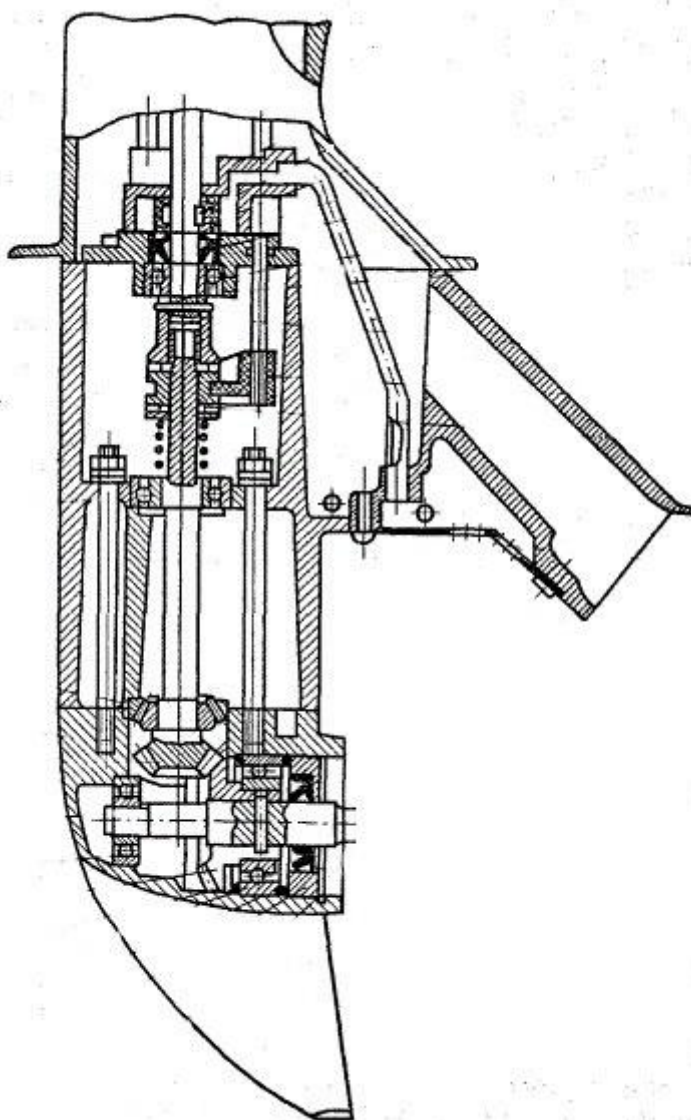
Фрагмент сборочного чертежа «Редуктор»
